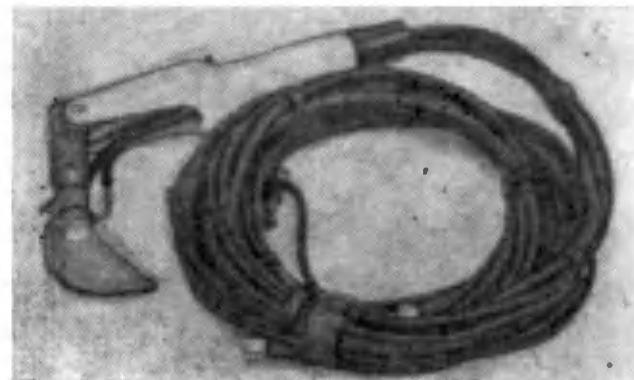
Аргонно-дуговая горелка с насадкой для сварки по щелевому зазору.
